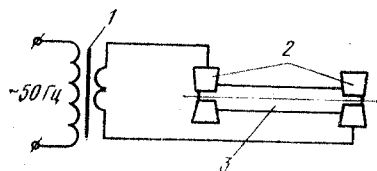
Принципиальная схема электроконтактного способа нагрева заготовок
